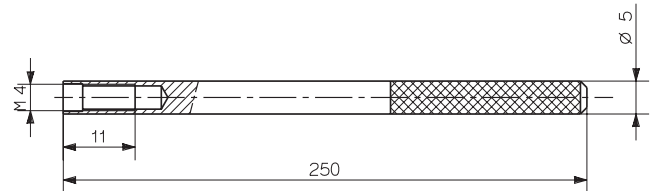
Ausziehwerkzeug für Blindsensor Typ 1319
